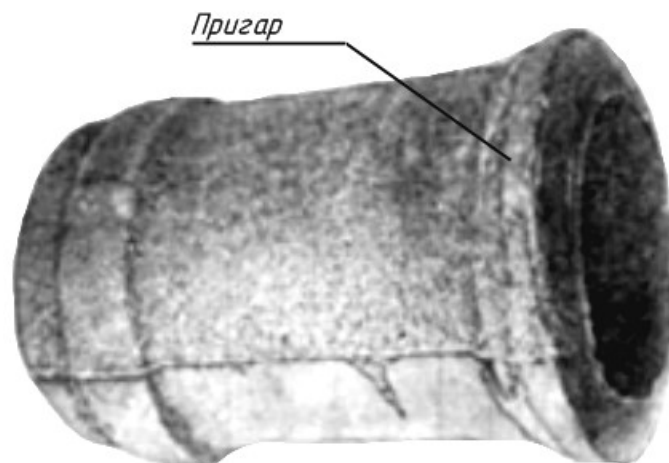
Отливка гильзы цилиндров с пригаром
